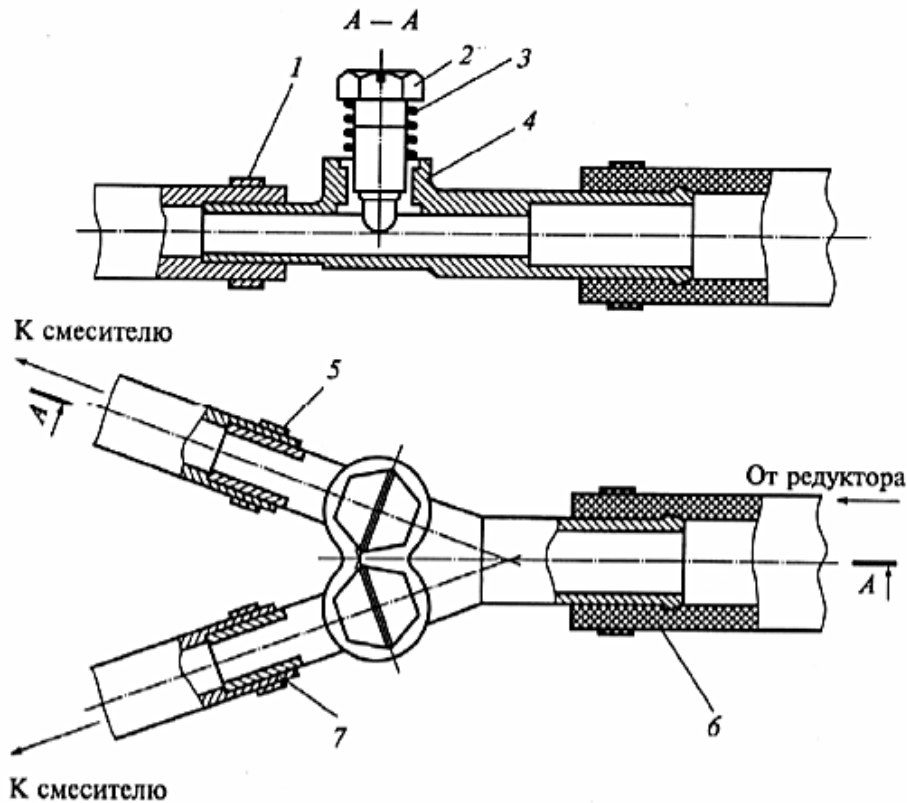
Тройник подвода газа: 1 - хомут; 2 - регулировочный винт; 3 - пружина; 4 - корпус тройника; 5 и 7 - патрубki подачи газа к смесителю; 6 - патрубок подвода газа.
